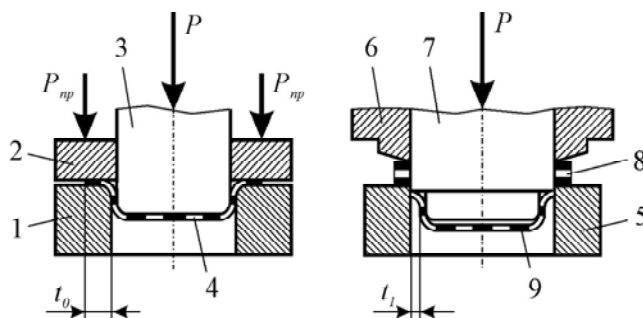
Схема робочої зони штампа для одночасного витягування та обрізування ковпачка із сітчастої заготовки
